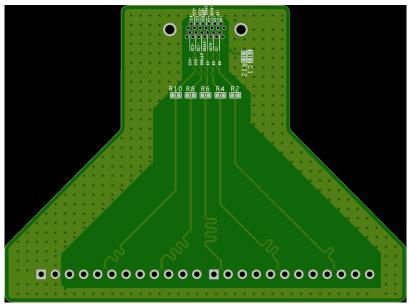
Hello-FPGA Camera link 接线板 PCB (成品包含连接器等器件)
